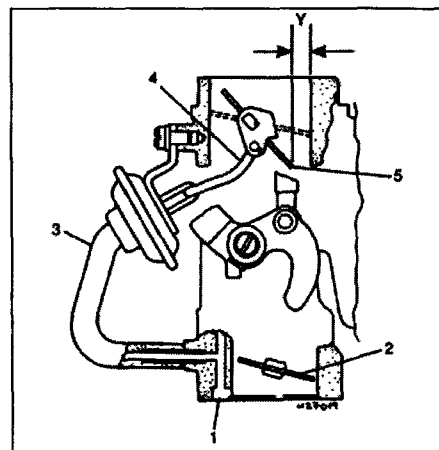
Регулировка пусковых оборотов - полуавтоматический привод
